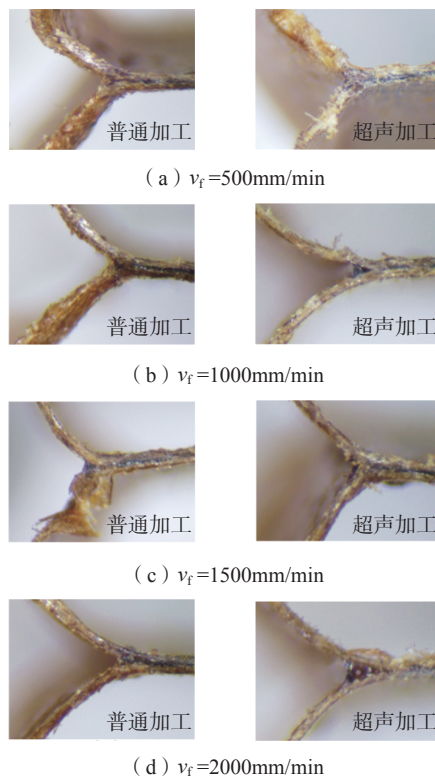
圆盘刀在不同加工方式下加工的蜂窝材料的表面形貌
